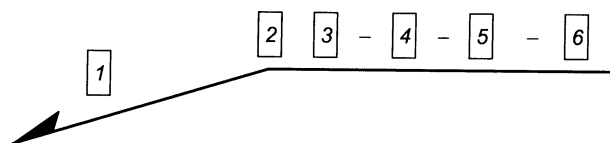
Структура условного обозначения сварного шва:
